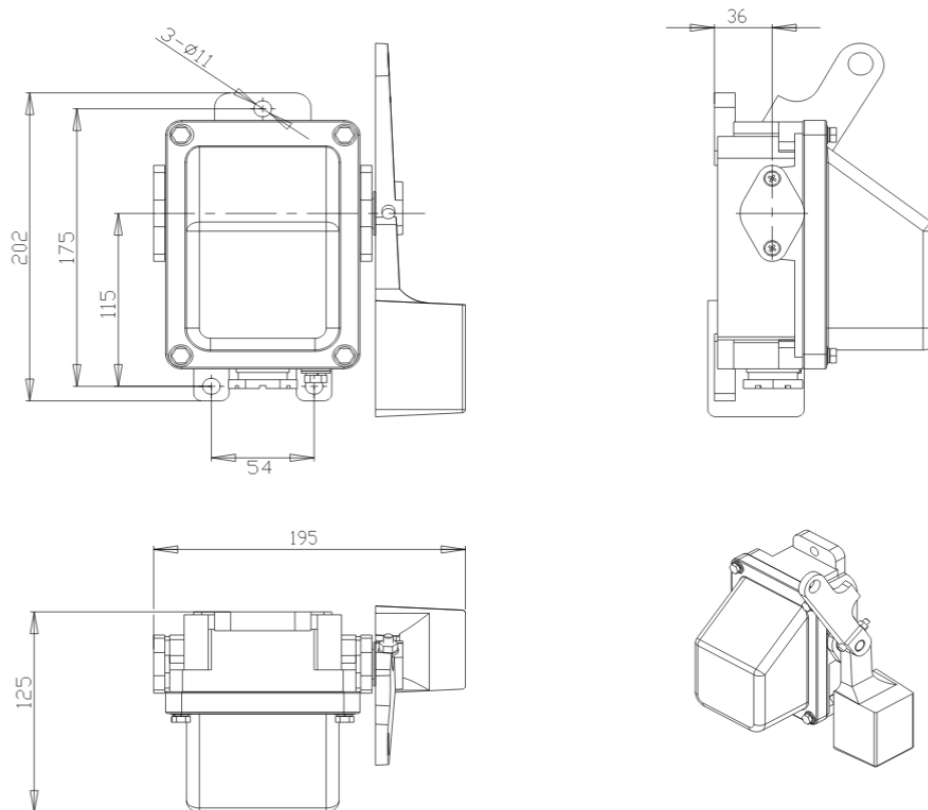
Габаритные размеры концевого выключателя КУ-703
